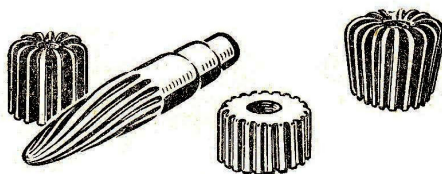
Фрези для обробки лопатей гребних гвинтів
